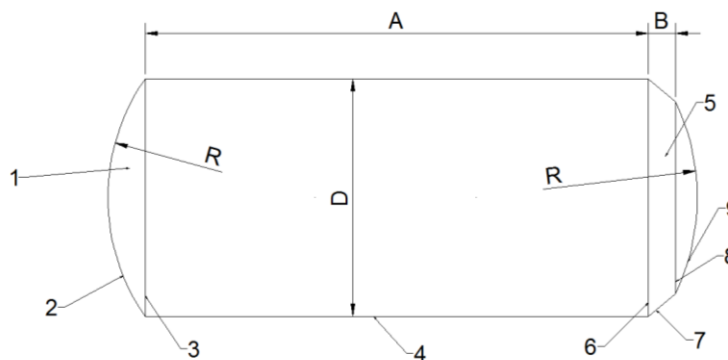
Конструктивно-силовая схема несущей топливной ёмкости первой ступени.
